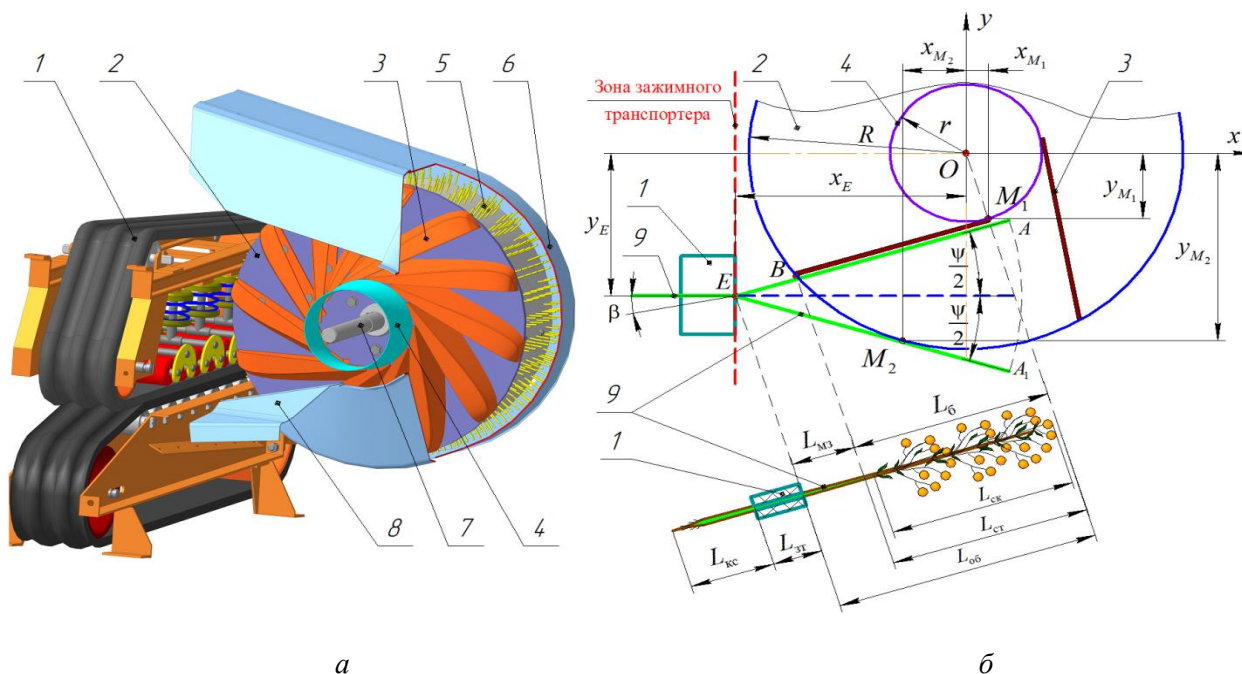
Общий вид устройства (а) и общая схема обмолота (б): 1 – зажимной транспортер; 2 – диск ротора; 3 – бич; 4 – защитное кольцо; 5 – вычесывающе-транспортирующая щетка; 6 – кожух; 7 – вал ротора; 8 – стол; 9 – стебли льна.
